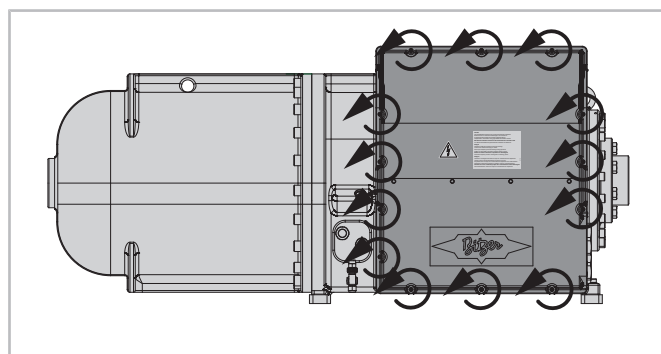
CSV.3: Снятие крышки корпуса FI.
